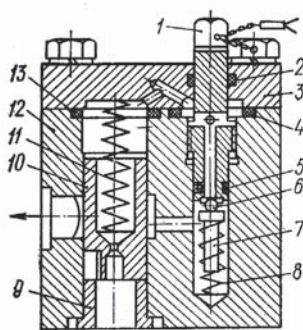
Запобіжний клапан непрямої дії: 1 — шпindelь; 2, 4, 5, 13 — гумові ущільнювальні кільця; 3 — кришка; 6 — кулька; 7 — шток; 8, 11 — пружини; 9 — втулка; 10 — поршень; 12 — корпус.
